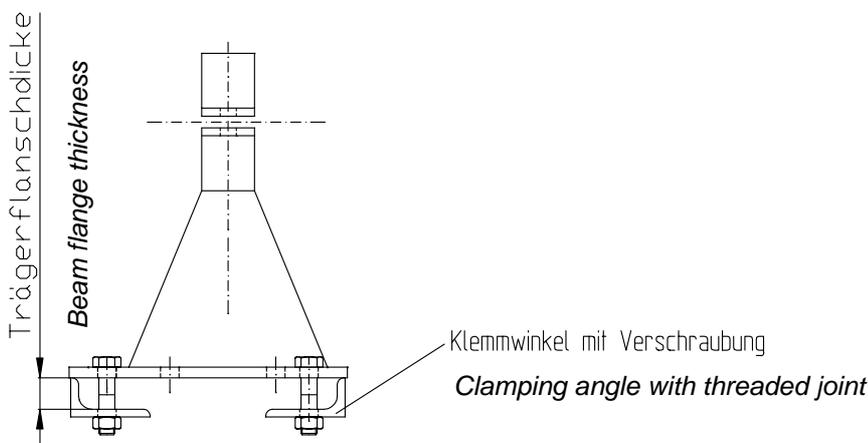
Trägerklemmbefestigung bei Befestigungsform A und C
